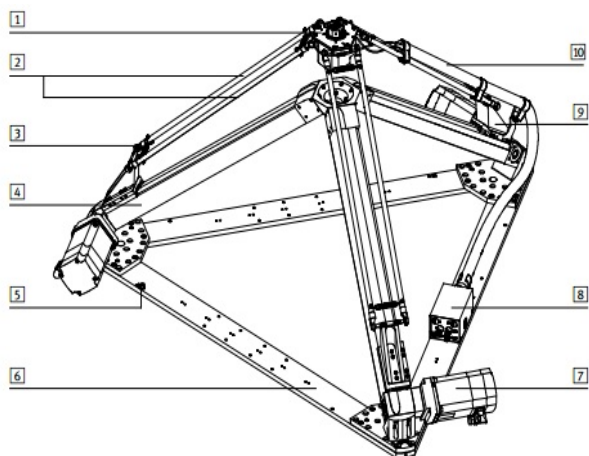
Конструктивная схема манипулятора типа «Трипод»: 1 — площадка захвата; 2 — триподная пара; 3 — шарнир; 4 — привод с зубчатым ремнём; 5 — зажим для подключения заземления; 6 — монтажная рама; 7 — мотор; 8 — корпус интерфейса; 9 — панель подключения; 10 — защитный шланг
